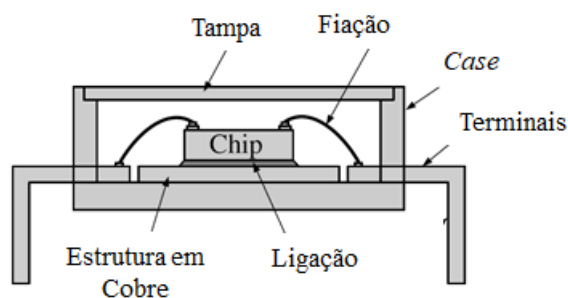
Os componentes de um encapsulamento comum de *chip*.
